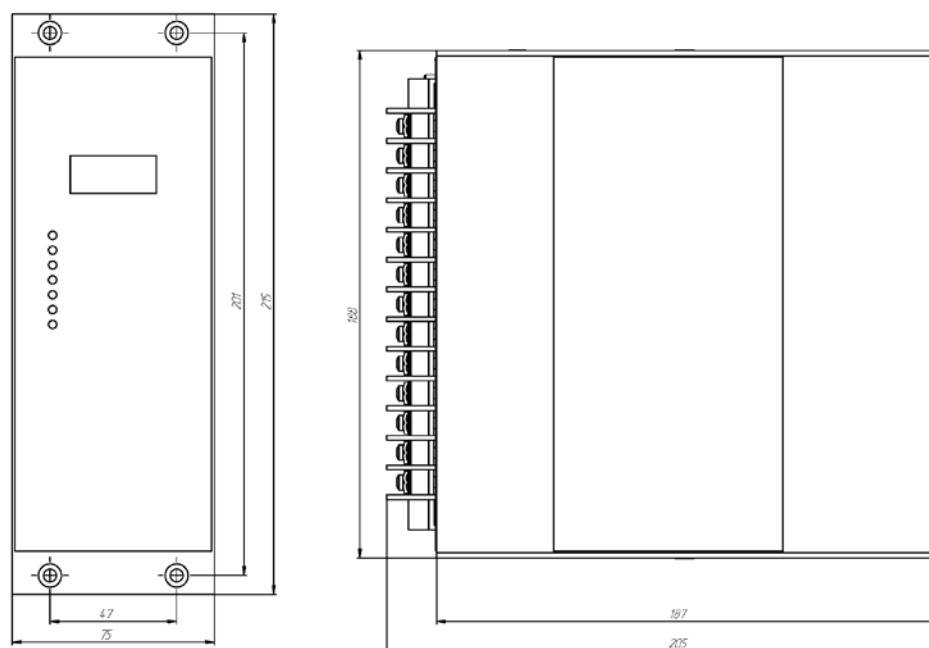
Габаритные и установочные размеры REST.02m в корпусе «У».
